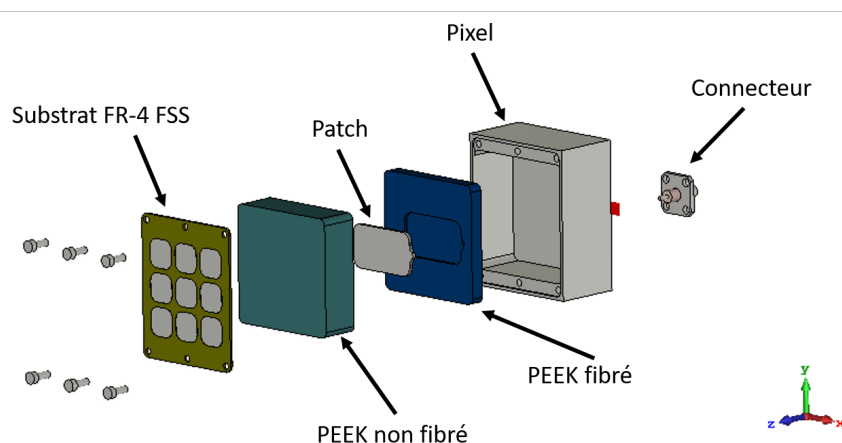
Vue éclatée du pixel dimensionné.
